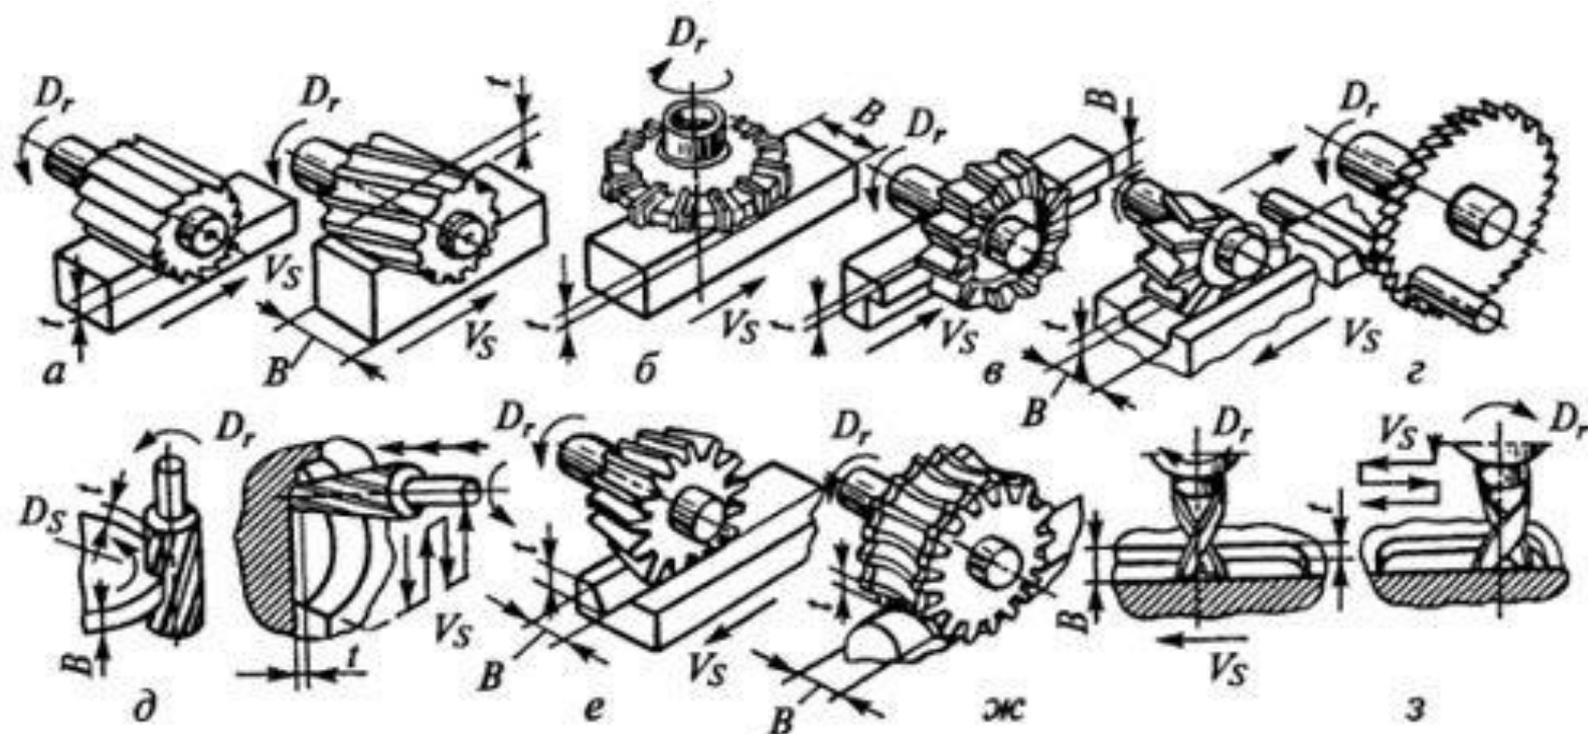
Виды работ, выполняемых фрезерованием, и применяемые фрезы:
